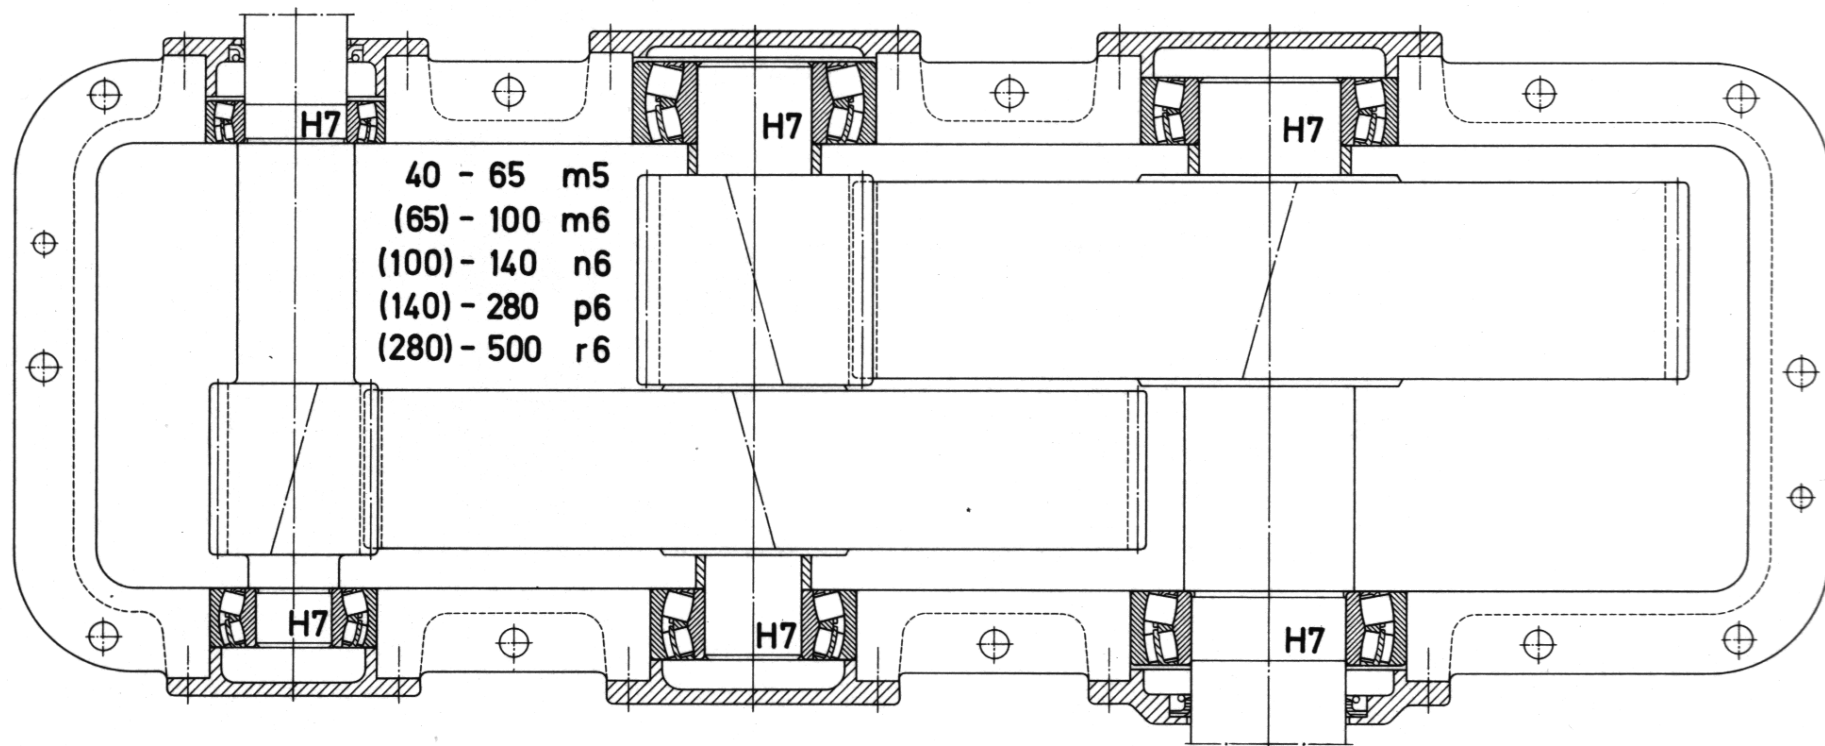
Redutor com engrenagem em parafuso.
